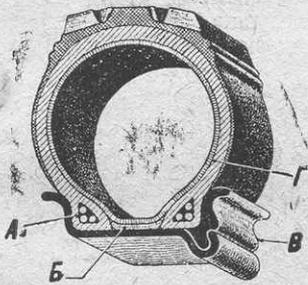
Разрез безбортовой покрышки на плоском обode со съёмным боковым кольцом.
